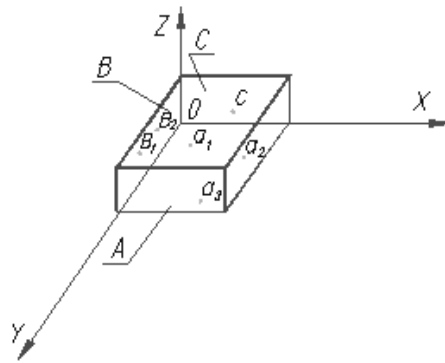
Схема расположения призматической заготовки в пространстве.
